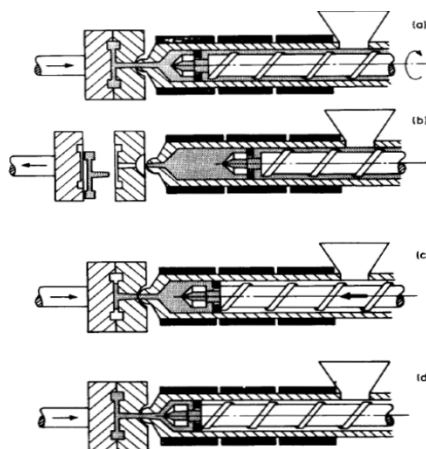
Ciclo típico de una máquina de tornillo recíproco.
